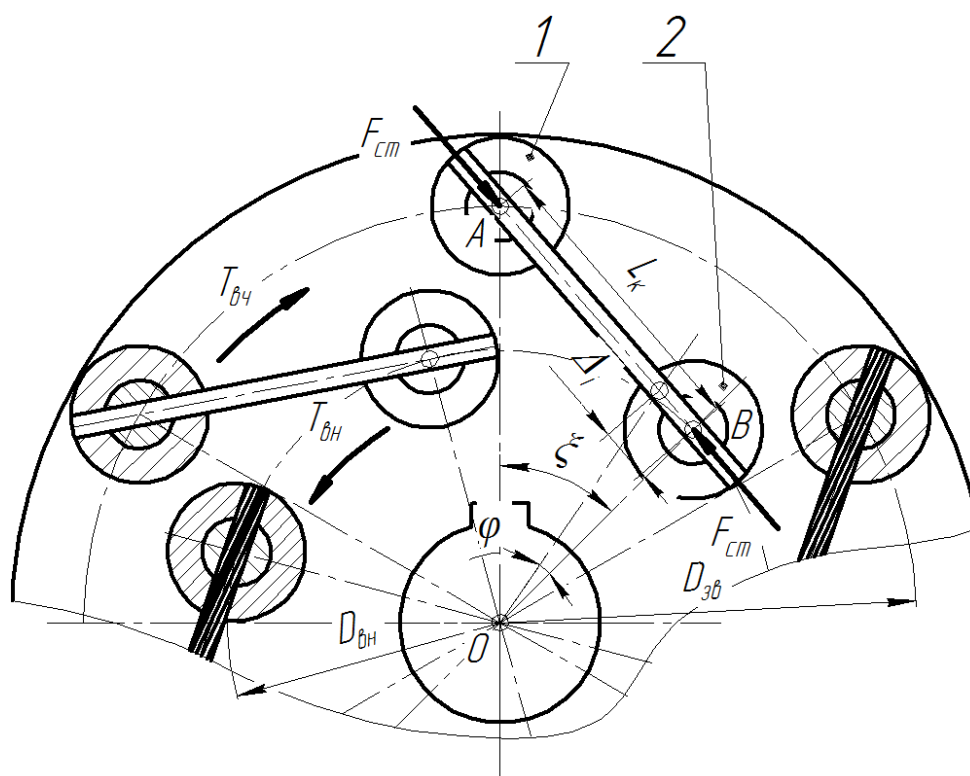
Розрахункова схема муфти з канатами тангенціального розташування в режимі реверсу
